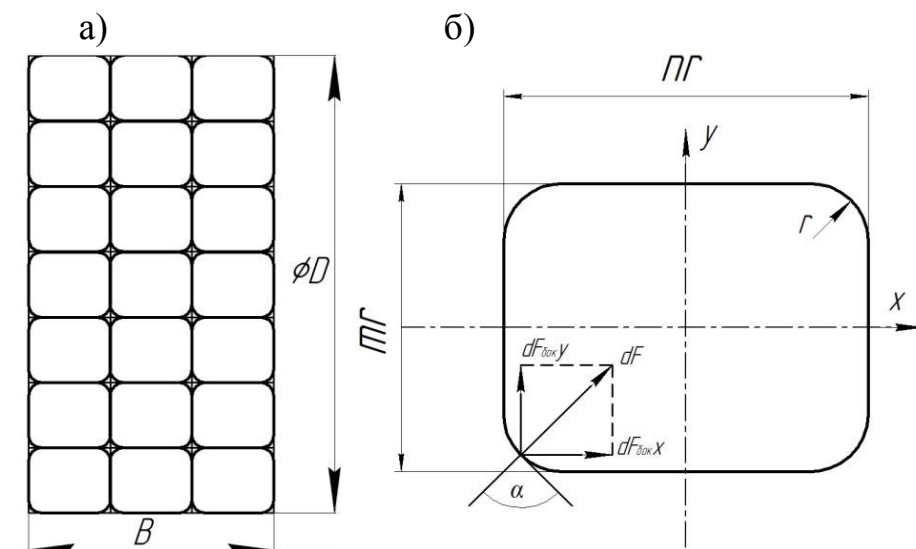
Рабочая поверхность банджа валка с наплавленной футерующей сеткой: а – общий вид; б – форма ячейки
